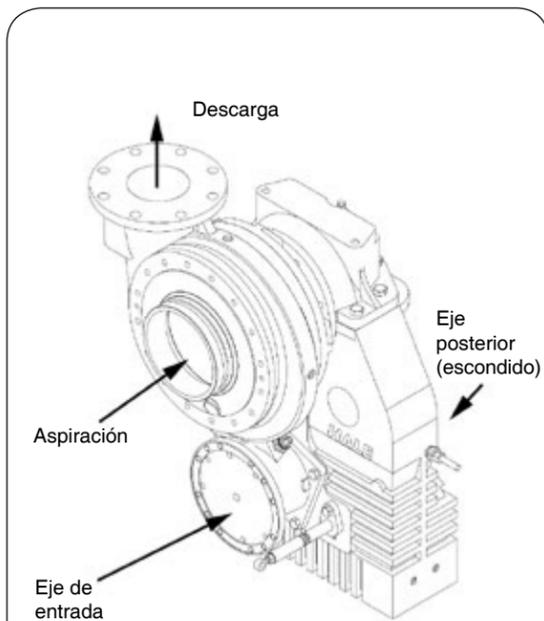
Conjunto de bomba DSD y caja de engranajes "G"
